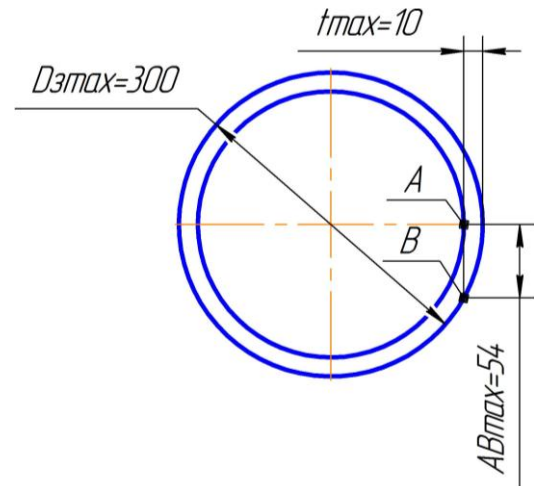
Размеры стружки при обработке проходным безвершинным сабельным резцом
